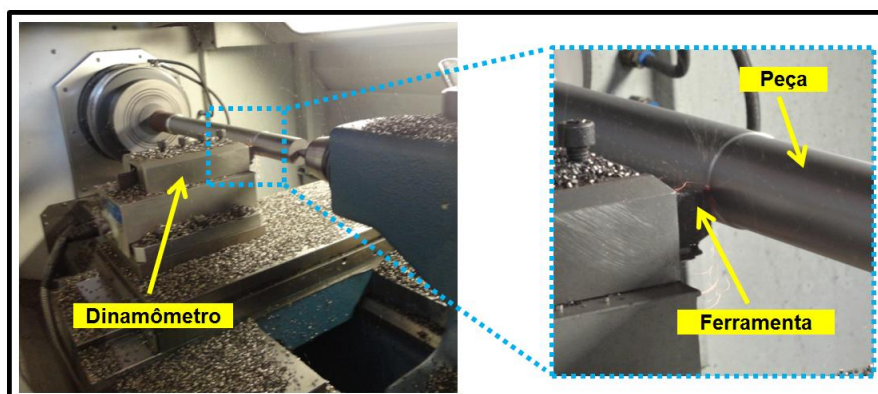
Montagem do dinamômetro no carro transversal do torno CNC
